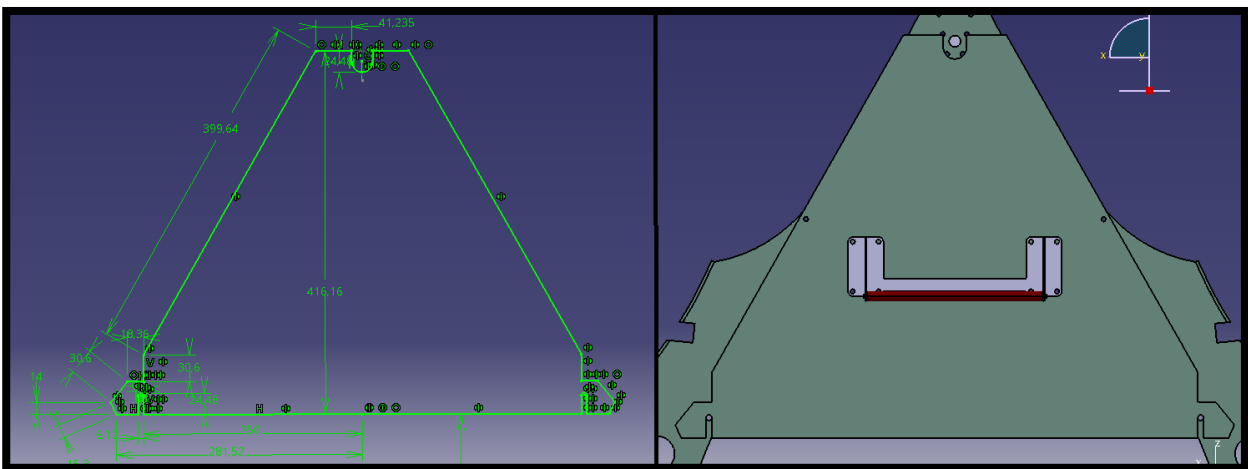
Head armour 11: Sketch y pieza final situada en el conjunto Costilla 11 tras extrusión y vaciado
